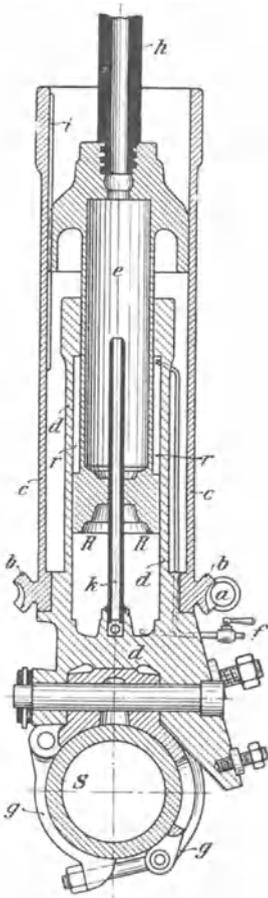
Schematischer Schnitt durch die Brandtsche Bohrmaschine.
